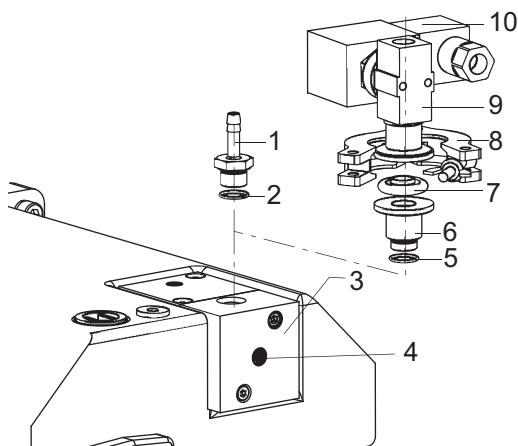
Anschluss des Magnetventils für das Gasballastventil (C-Version)
